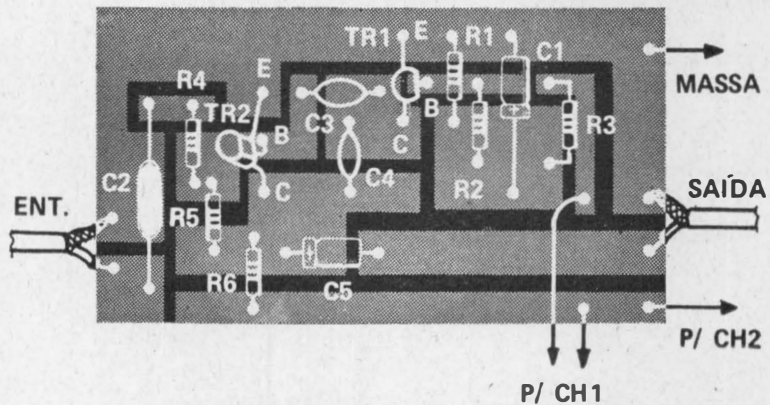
Disposição dos componentes sobre a plaqueta da Fig. 2.
